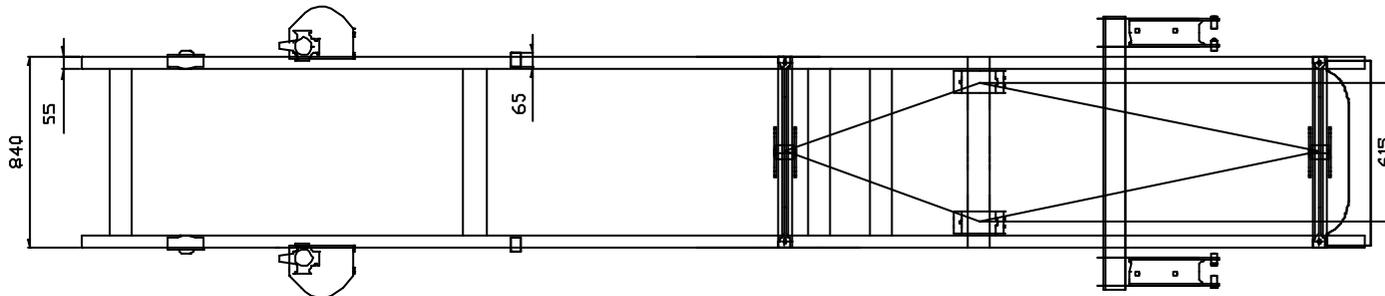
2x3-Lagerung beim langen Radstand mit Befestigungsteile für Fremdaufbauten (D 65), U3000 - U5000
